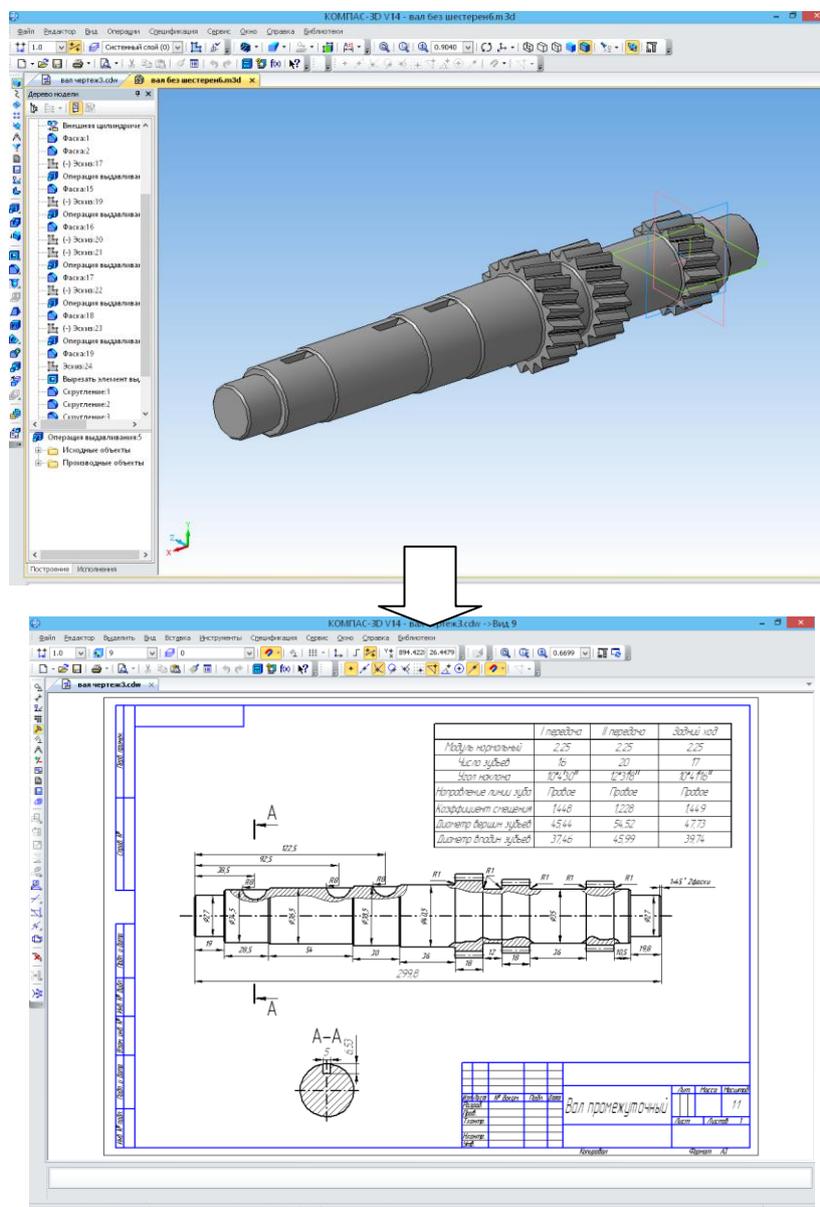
Получение чертежа промежуточного вала коробки передач с помощью 3D модели
